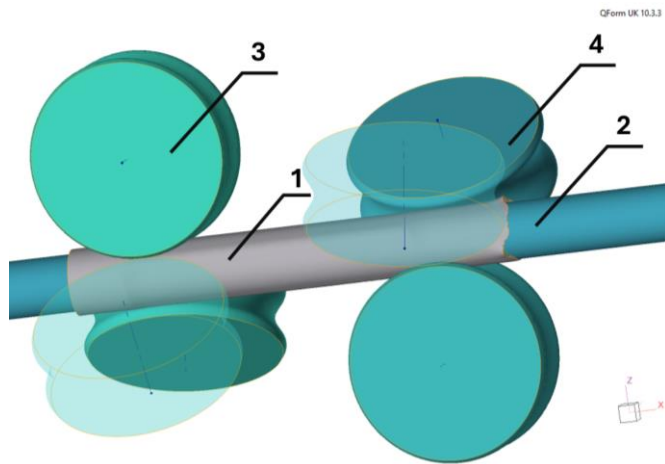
Креслення інструменту та заготовки при моделюванні в QForm UK:
